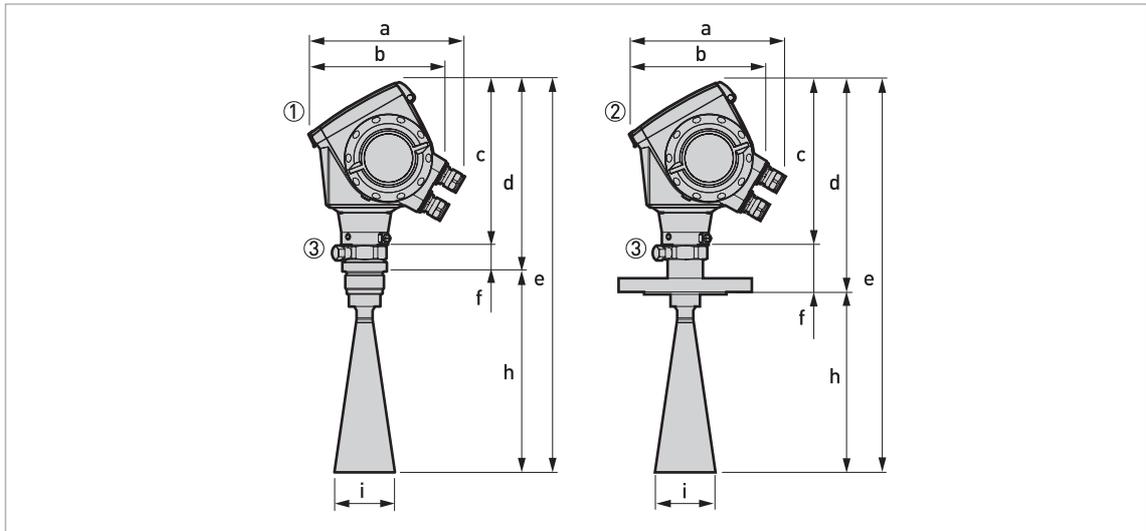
Versions d'antenne roulée/soudée DN80/3", DN100/4", DN150/6" et DN200/8"
